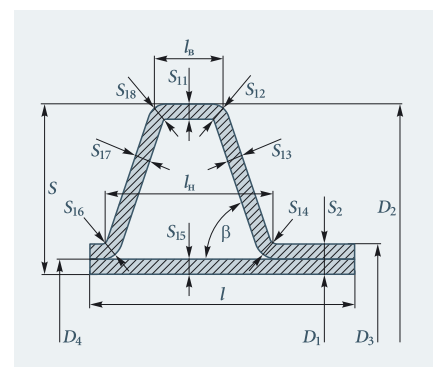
Схема гофра полиэтиленовой трубы с двойными стенками с основными размерными характеристиками
